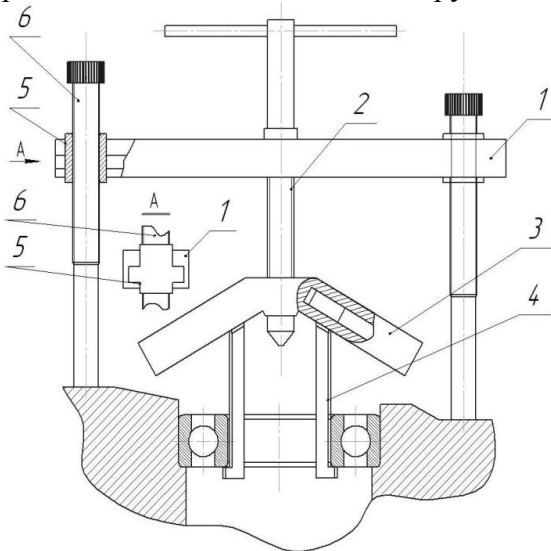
Схема демонтажу підшипника з отвору знімачем з самозатискними лапами циліндричної форми
